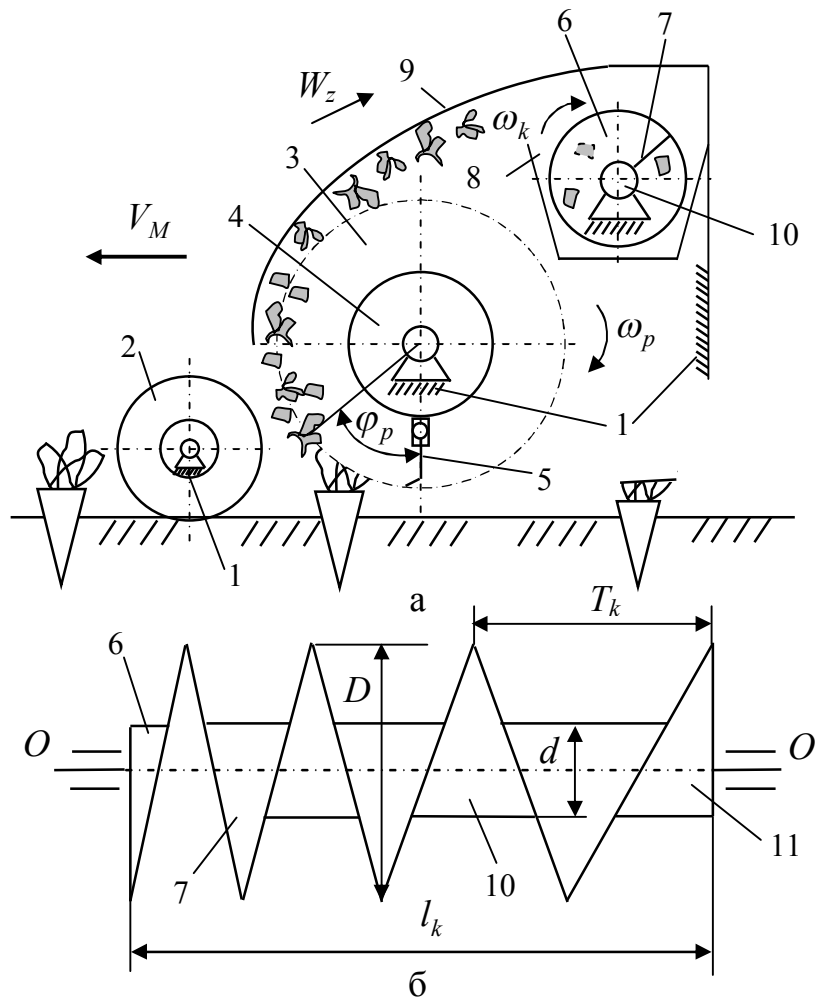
Схема для розрахунку продуктивності роботи шнекового конвеєра: а – схема процесу роботи; б – схема шнекового конвеєра; 1 – рама; 2 – колесо опорне; 3 – роторний гичкоріз; 4, 10 – барабан; 5 – ніж; 6 – шнековий конвеєр; 7 – виток; 8 – жолоб; 9 – кожух; 11 – вихідна частина шнека
